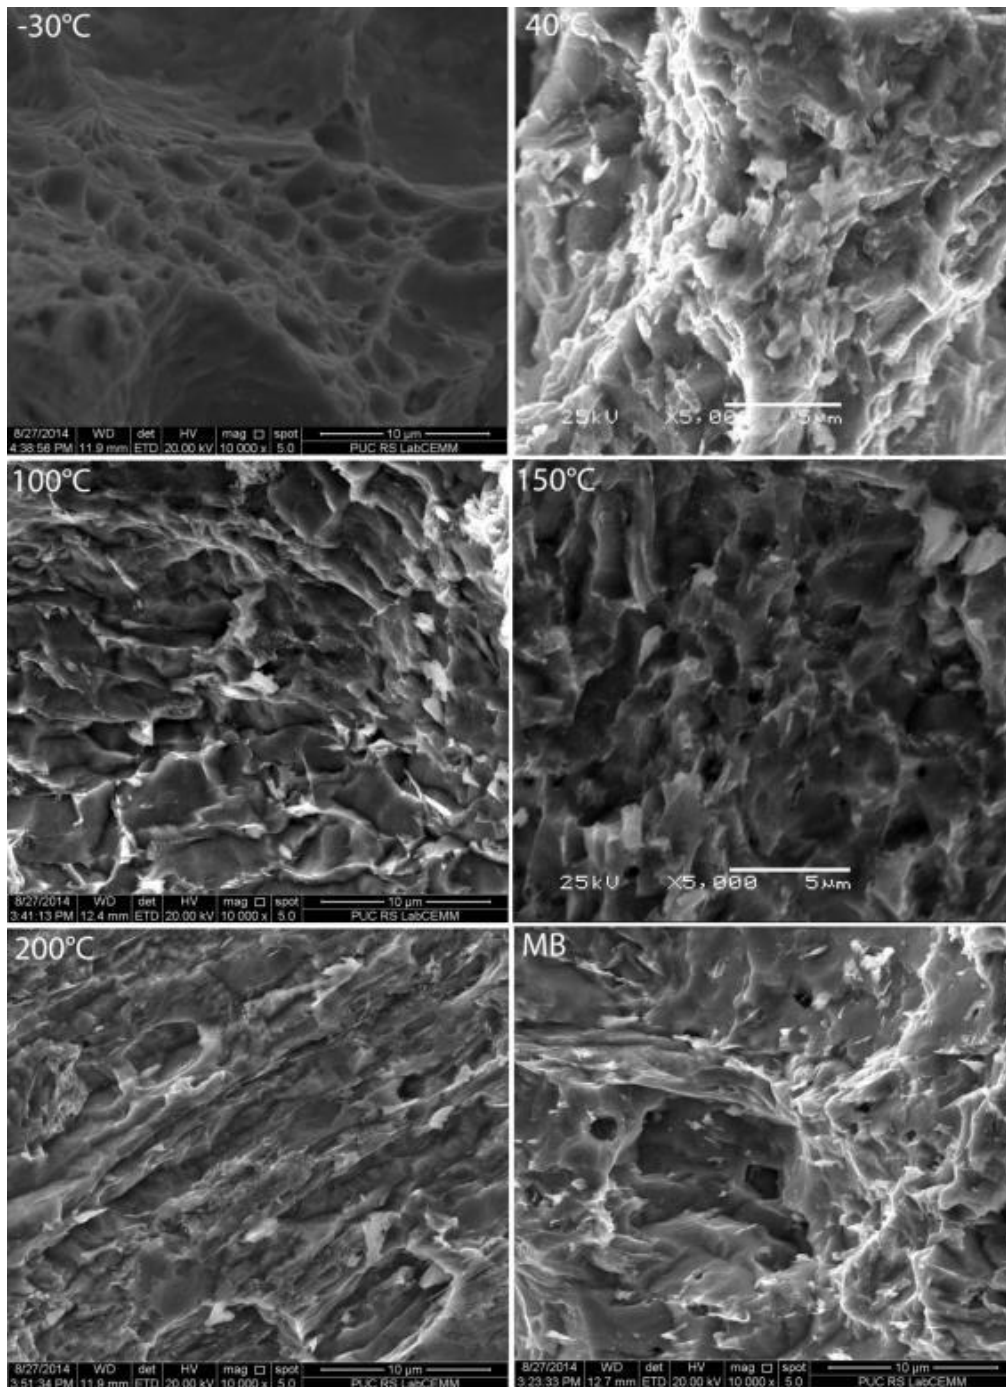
Imagens do MEV das superfícies de fratura das amostras após o ensaio de Impacto Charpy-V realizada a - 40 °C. O número posicionado no canto superior esquerdo de cada amostra indica a temperatura de pré-aquecimento da soldagem e MB é metal base.
